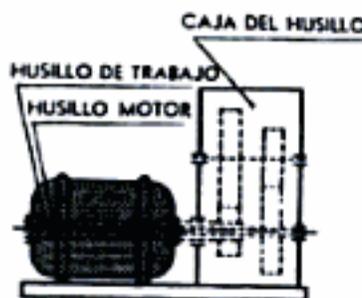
,5 Motor con eje hueco; transmisión de la fuerza por medio de ruedas dentadas
